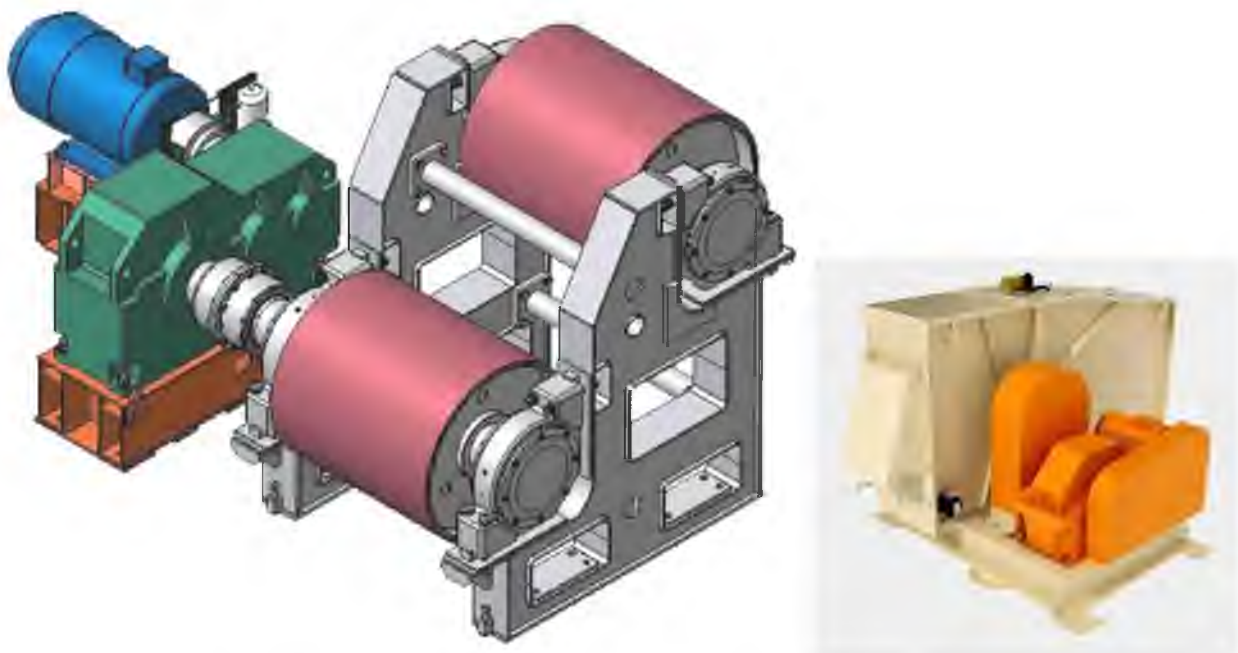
Внешний вид редукторной приводной станции ленточного транспортера
